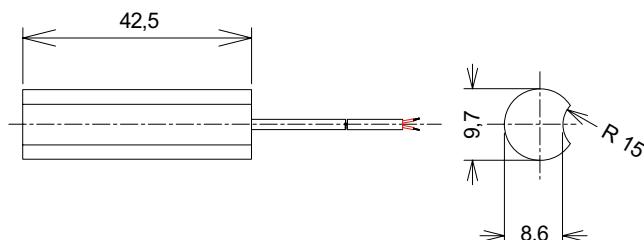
Габариты датчика рециркулирующего потока Norm-NTC-2 в металлическом корпусе
